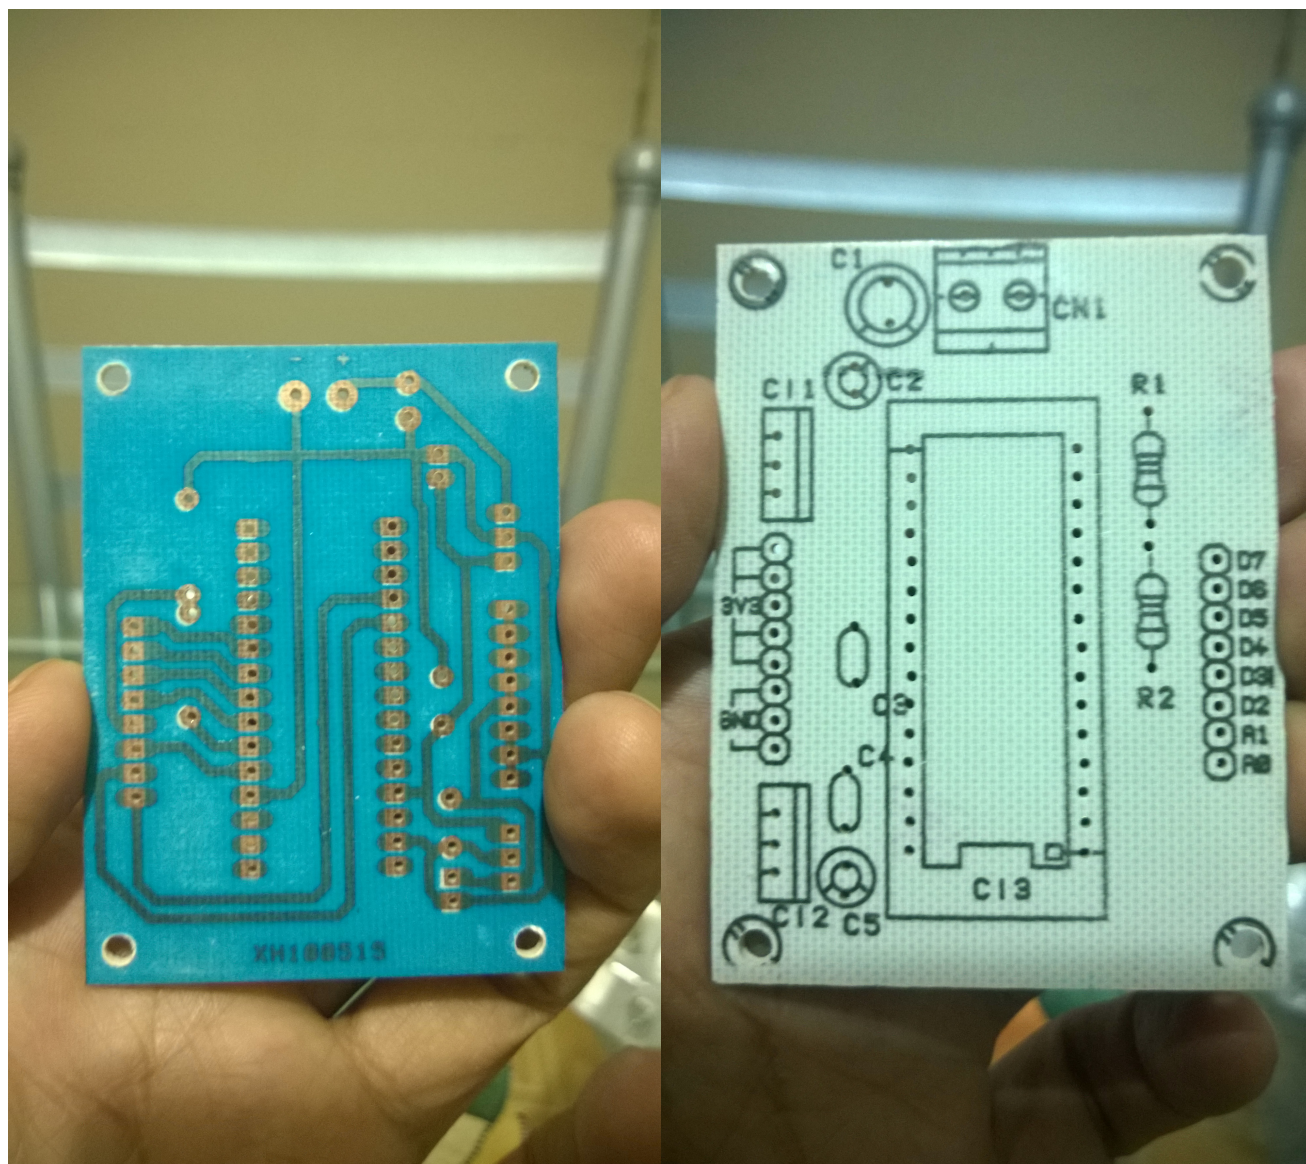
Circuito impreso sin componentes. Las medidas del circuito impreso fueron 51x67mm y 2mm de altura. Con los componentes soldados a la placa, el circuito aumenta su altura a 33mm, por lo tanto la carcasa debe tener cuando menos estas medidas: 51x67x33mm.
